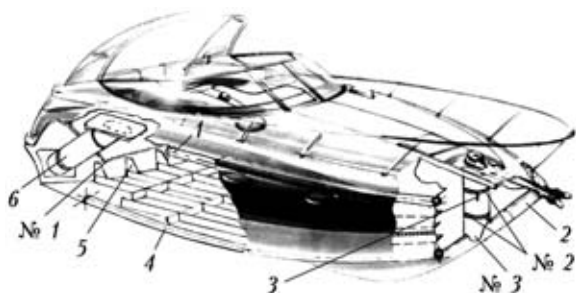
Схема сварной конструкции корпуса ТК из сплава АМгб: 1 — усиление палубы; 2 — носовая оконечность киля; 3 — носовая стойка; 4 — усиление днища; 5 — кница; 6 — кормовая стойка; № 1 — шов усиления кормы; № 2 — шов стойки; № 3 — шов крепления стойки на форштевне
